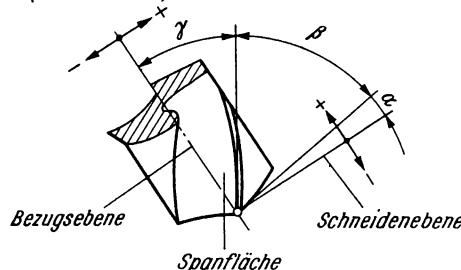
Winkel im Werkzeugbezugssystem am Spiralbohrer
